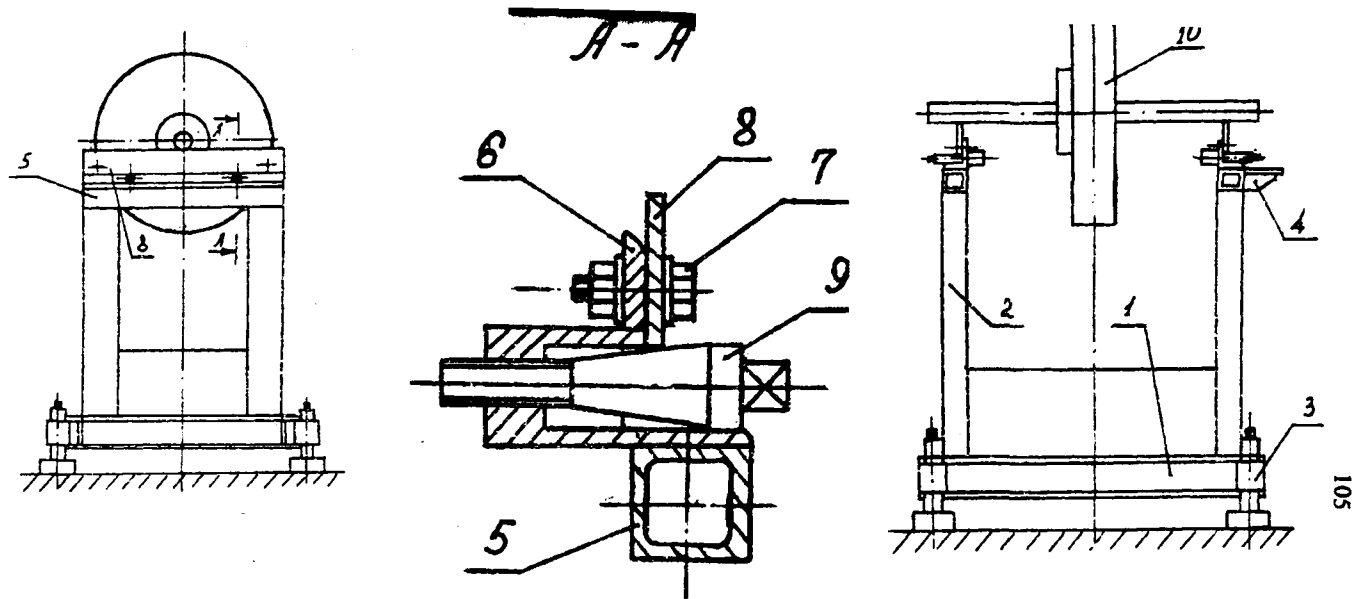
Схема лабораторного стенда для статической балансировки роторов
